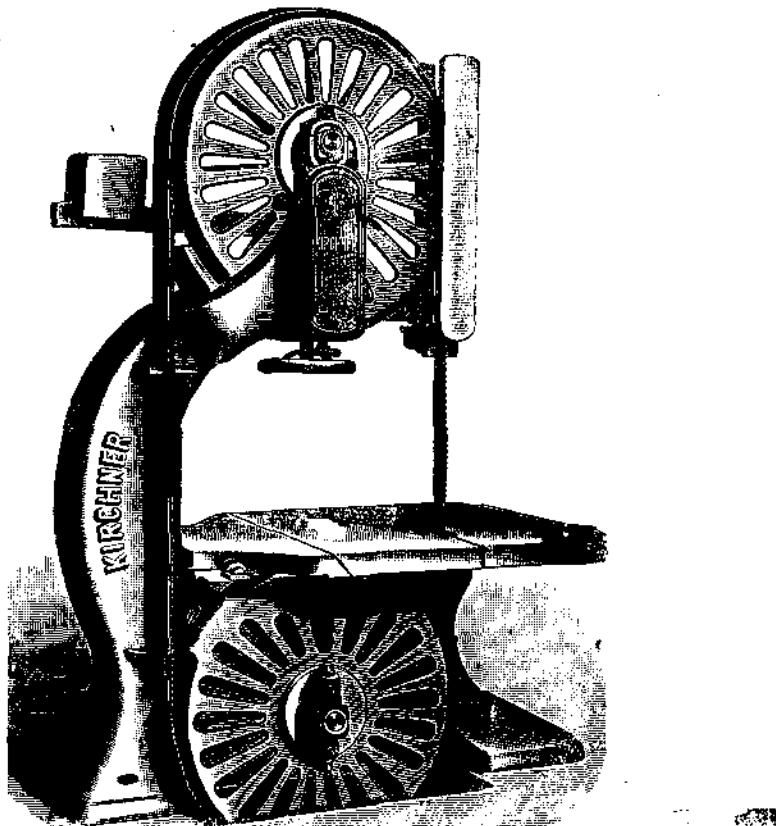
Предохранительные приспособления в станках с ленточными пилами.
